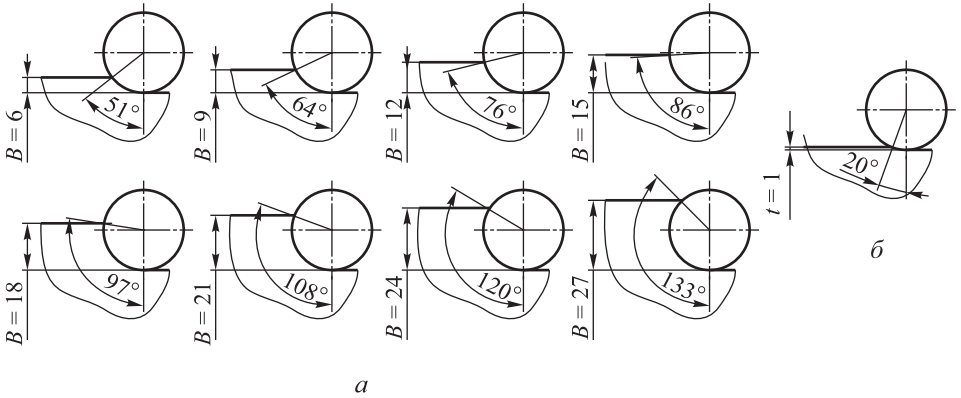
Геометрическое определение угла контакта зуба фрезы с заготовкой при одном резе при торцовом (а) и цилиндрическом (б) фрезеровании
